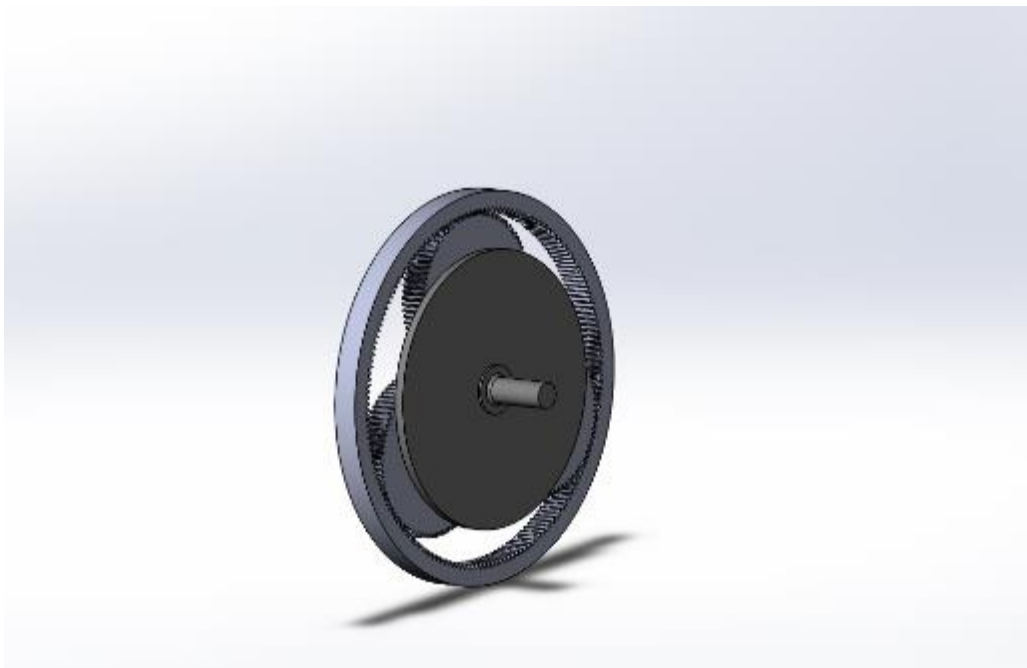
3 ступень планетарного редуктора с выходным валом
